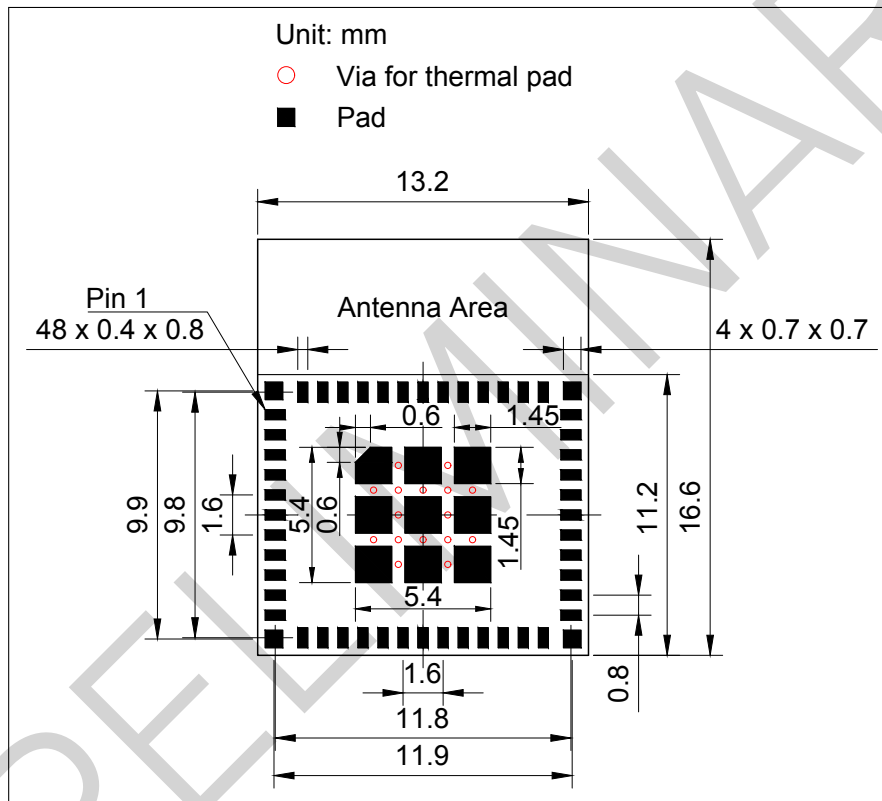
ESP32-C61-MINI-1 推荐 PCB 封装图形
